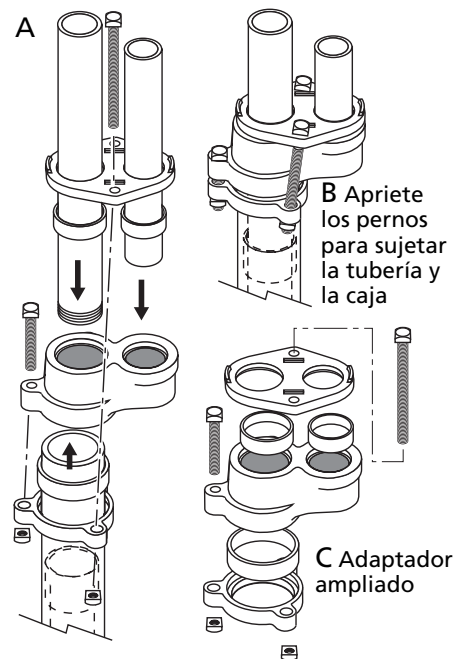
Conjunto del Adaptador de la Caja para el Paquete 4HFC2
